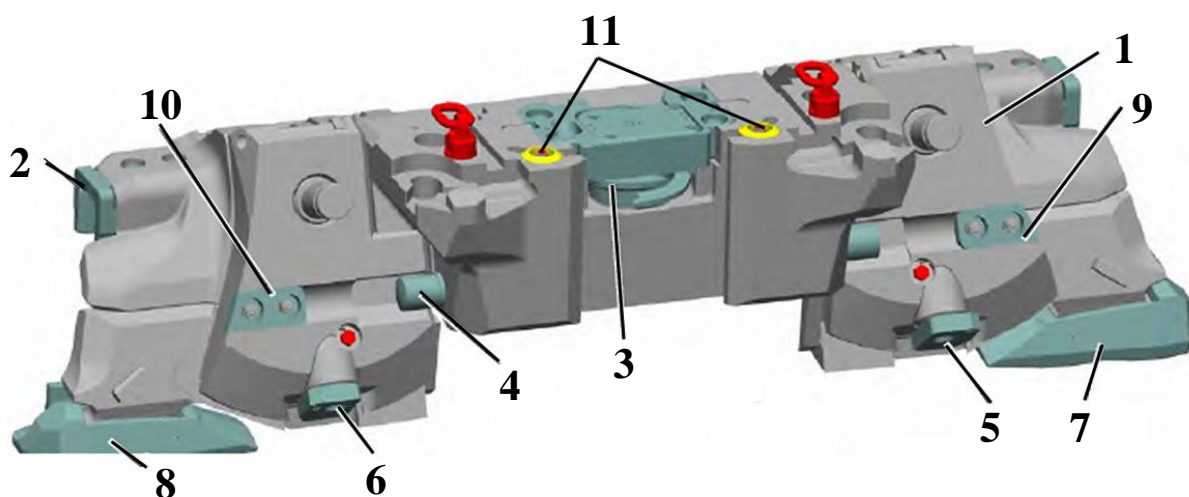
Корпус струга скользящего типа GH 9-38/5.7 N
